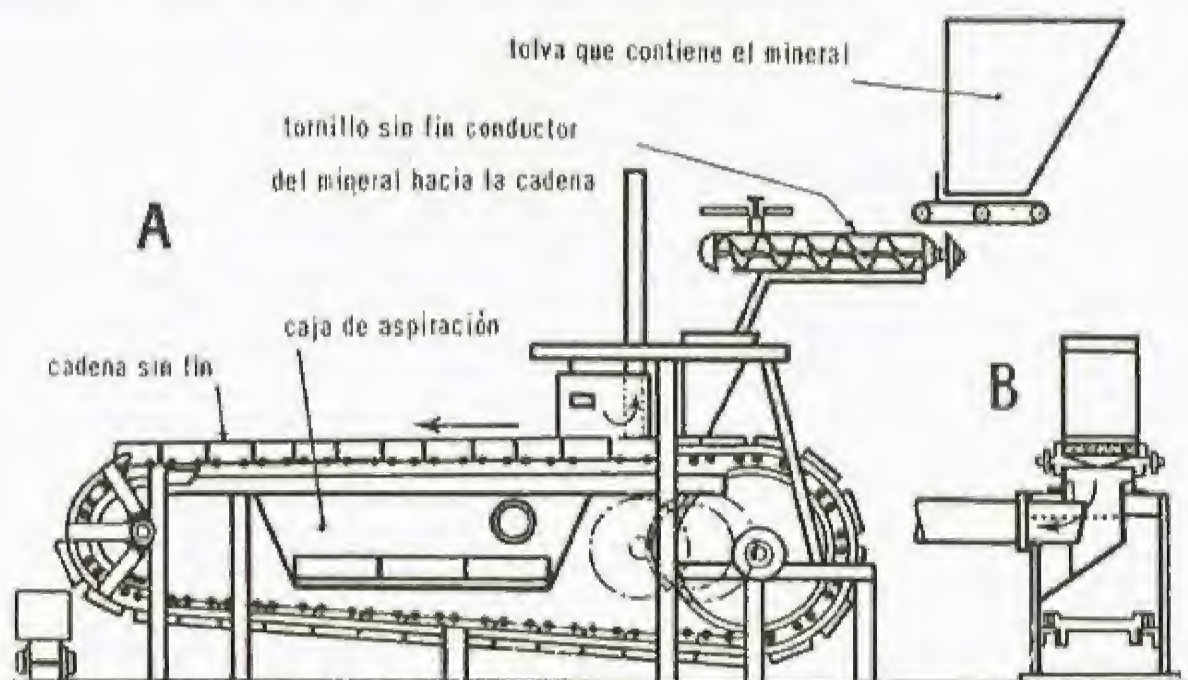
Procedimiento Dwight y Lloyd. Aparato de cadena sin fin: A. Alzado; B. Corte
